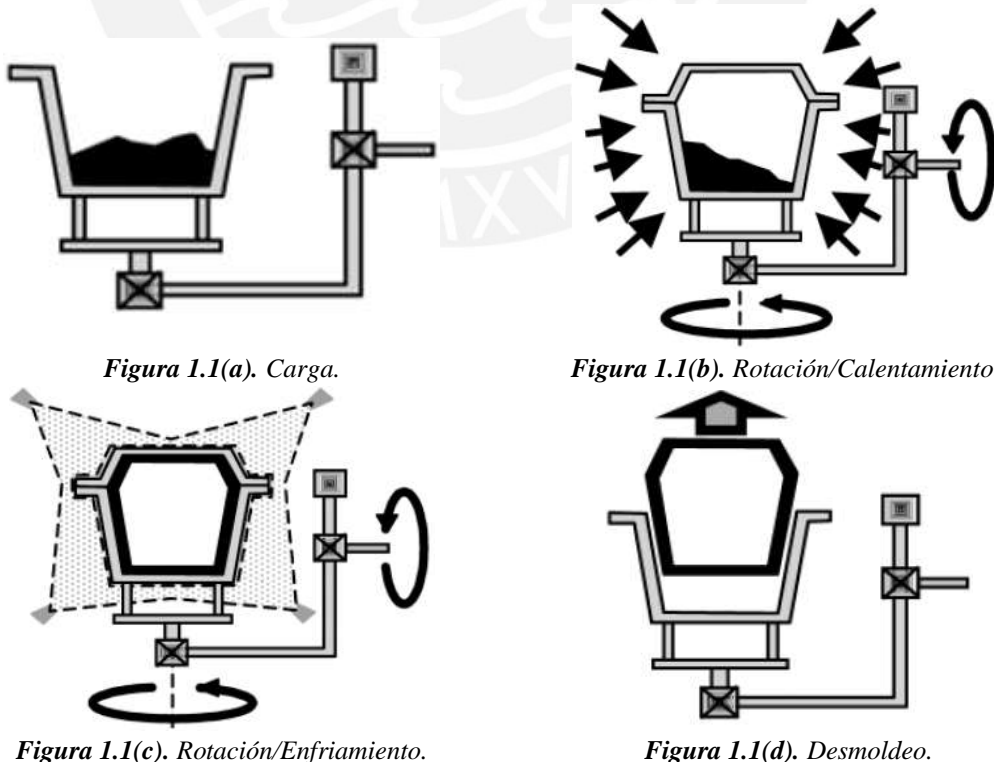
Etapas del proceso de moldeo rotacional [4].
